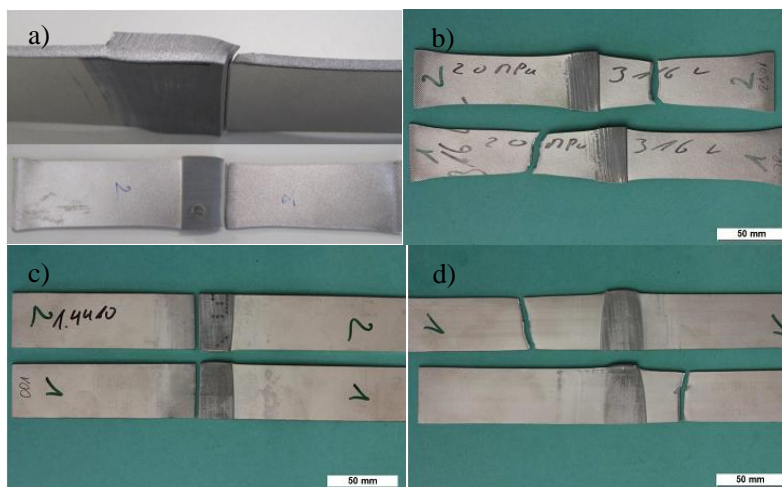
Ensaio mecânico: a) AISI 316L soldada com 35MPa, b) AISI 316L soldada com 18MPa, c) UNS 32750 e d) UNS 31803.
